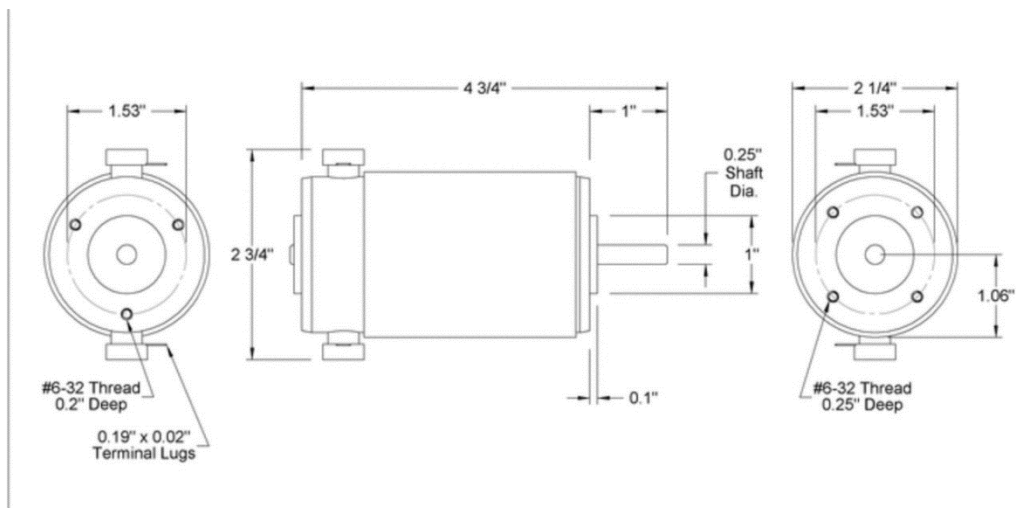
Dimensiones del motor del sistema de movimiento de la espátula
